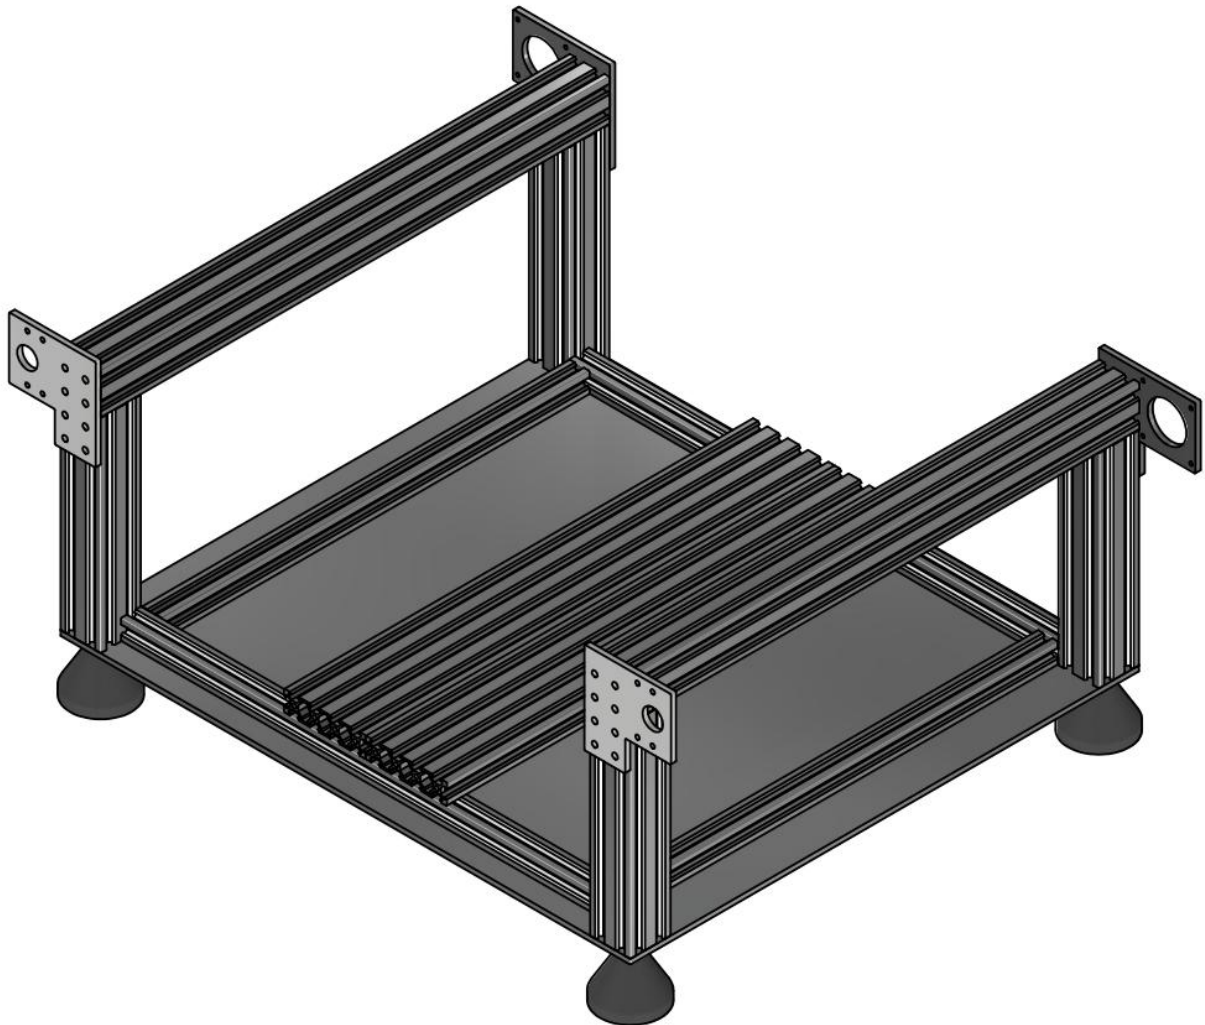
Загальний вигляд станини у формі U-подібної конструкції
